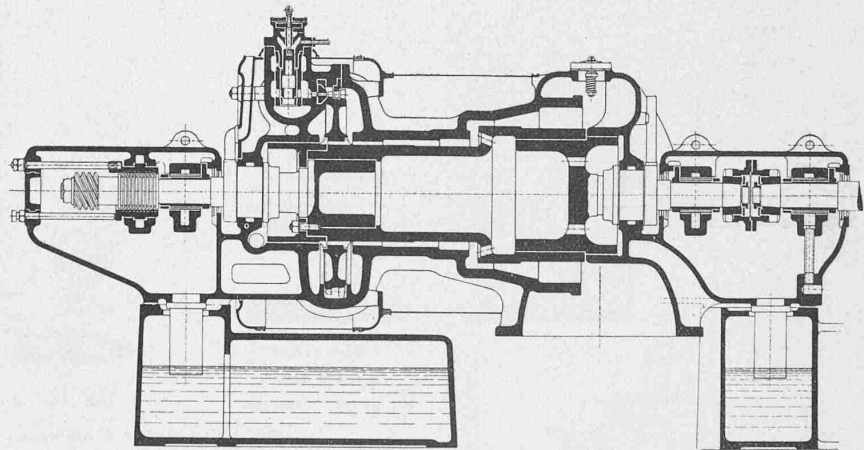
Dampfturbine nach Bauart Brown, Boveri & Cie., Baden. — Etwa 1:40.
